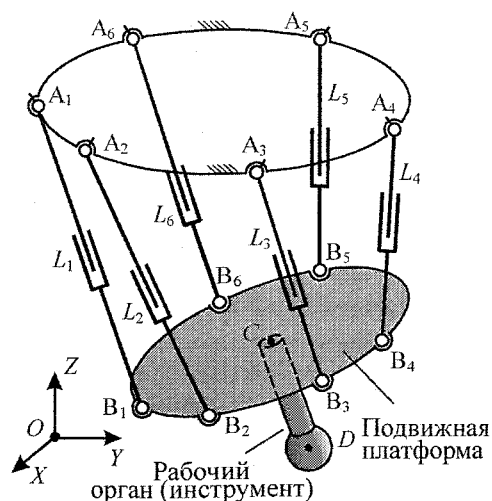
Кинематическая схема ОПК, обеспечивающего движение рабочего органа по шести координатам
